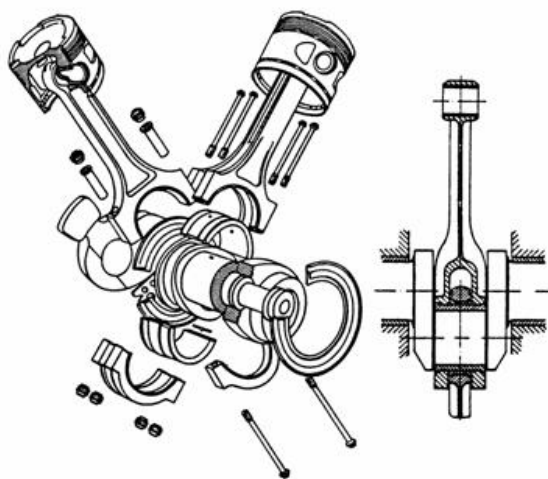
Modul de montare a ambielajului în furcă la un motor în V
